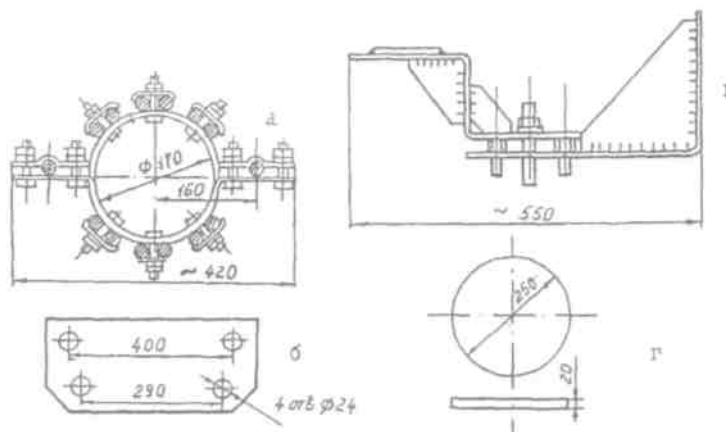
Типовые детали для гибких связей: а – распорное кольцо серии КТП; б – коромысло; в – держатель; г – контактный диск
